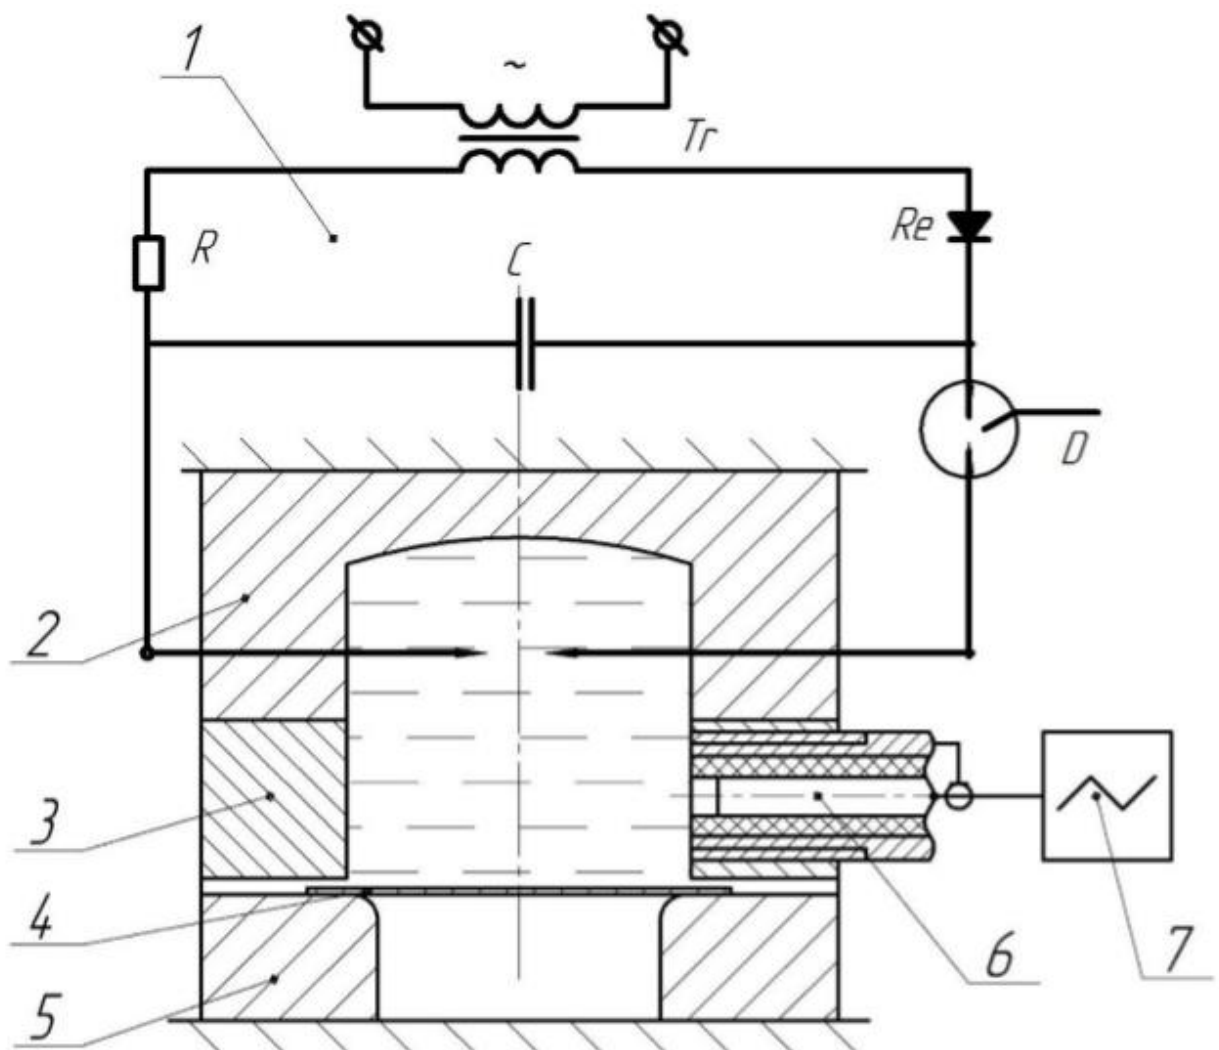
Схема ЕГД витяжки листового металу, що містить у собі датчик для вимірювання імпульсного тиску: 1 – ЕГД установка; 2 – розрядна камера; 3 – вкладка з п'єзоелектричним датчиком; 4 – листова заготовка; 5 – матриця; 6 – датчик для вимірювання тиску; 7 – осцилограф
